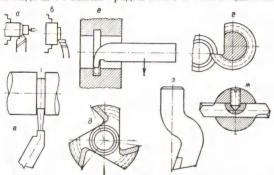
Некоторые типы резцов: a— токарный проходной прямой;  $\delta$ — токарный подрезной отогнутый;  $\epsilon$ — токарный прорезной отогнутый;  $\epsilon$ — токарный круглый;  $\partial$ — токарный фасонный твердосилавный; e— расточный для внутренних канавок; w— расточный двухлезвийный; s— строгальный подрезной.
